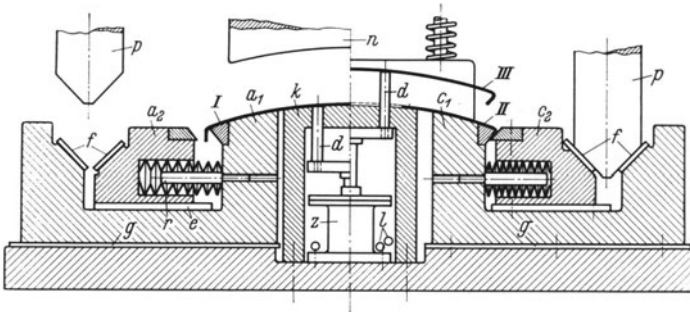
Mit Gleitplatten bestücktes Umkantwerkzeug zu Abb. 235
